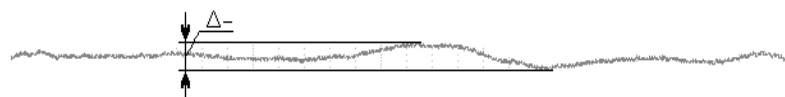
Профиліограми оброблених поверхностей після зустрічного циліндричного фрезерування з різними частотами обертання шпинделя
